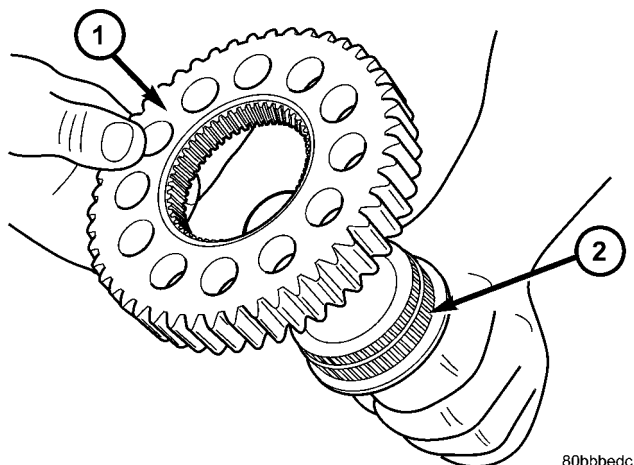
Retire el engranaje propulsor del eje transmisor delantero
